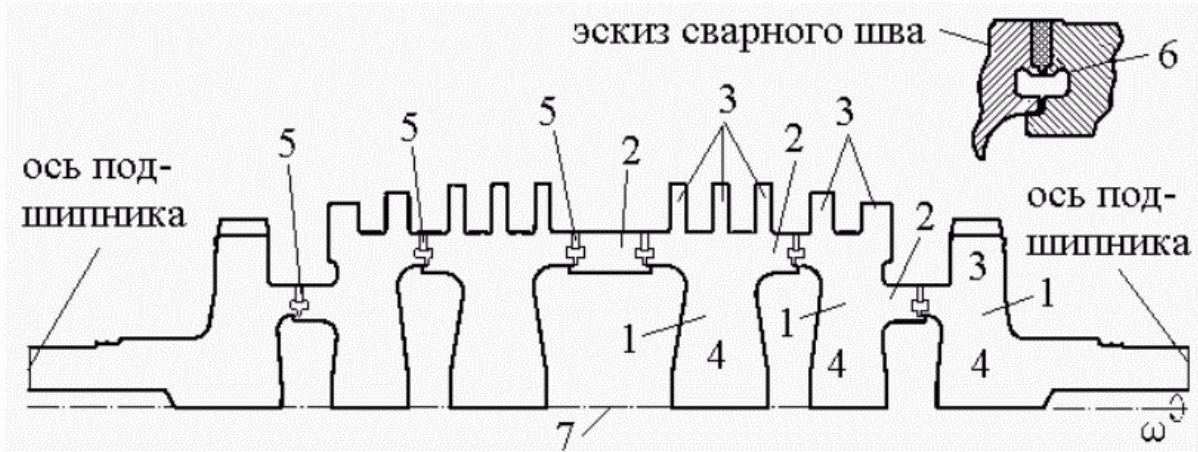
Сварной ротор паровой турбины. 1 - кованые диски; 2 - перемычки; 3 - наружные части дисков; 4 - внутренние части дисков; 5 - сварные швы; 6 "деконцентраторы" напряжений; 7 - ось вращения ротора.
